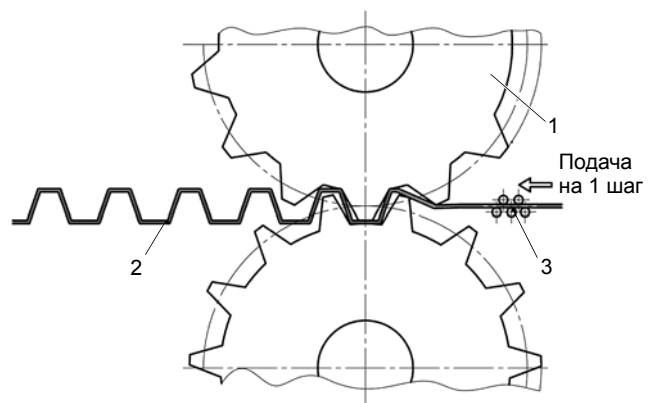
Схема формирования гнутого зубчатого сегмента из стального проката на гибочной машине с зубчатыми вальцами: 1 — вальцы с зубчатым профилем специальной формы; 2 — готовый гнутый зубчатый профиль; 3 — механизм подачи исходного проката
